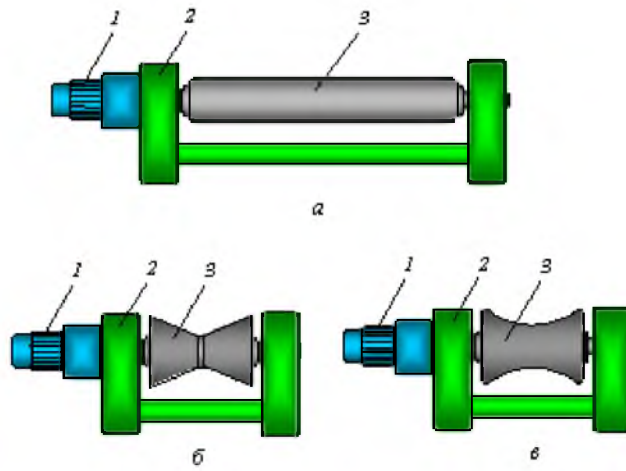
Рольганги с индивидуальным приводом и роликами: а — цилиндрическим; б — биконическим; в — профильным; 1 — мотор-редуктор; 2 — подшипниковая опора; 3 — ролик
